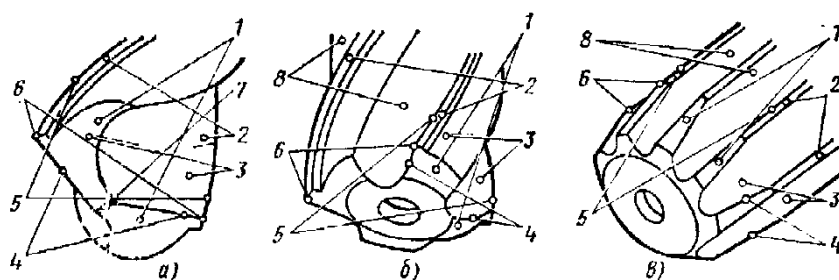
Элементы режущей части сверла (а), зенкера (б)
